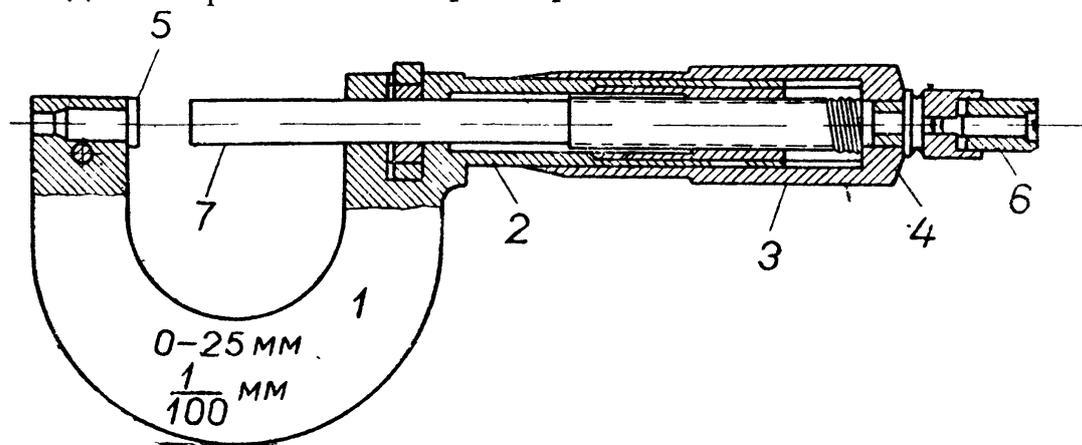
Микрометр: 1—скоба; 2—трубка; 3—микрометрический винт; 4—гильза; 5—наковаленка; 6—трещотка; 7—гладкий конец винта
